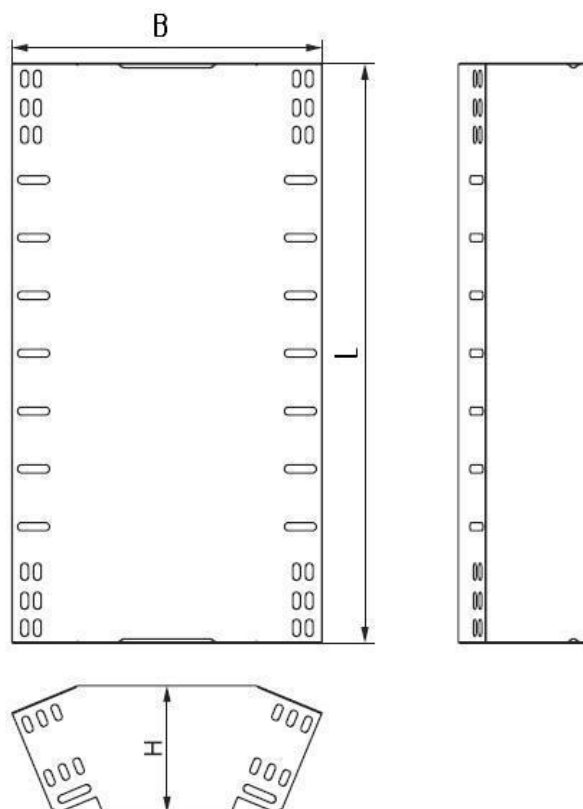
Поворот на 45° вертикальный внутренний.
